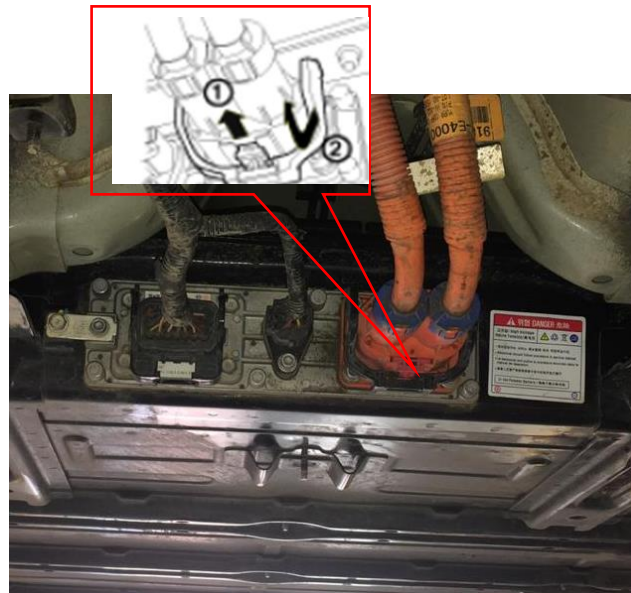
Desmontaje del cable de alto voltaje. Fuente: Autores.
